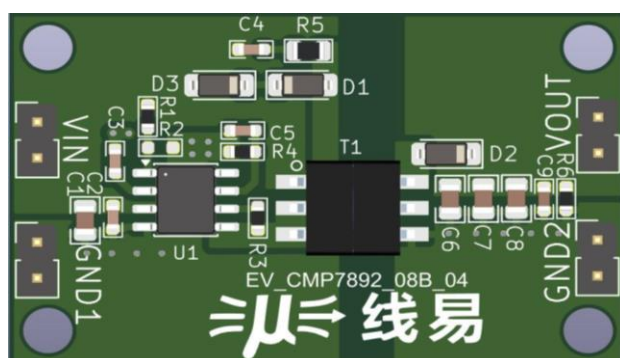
PCB 示意图 (尺寸: 25x 45mm)
